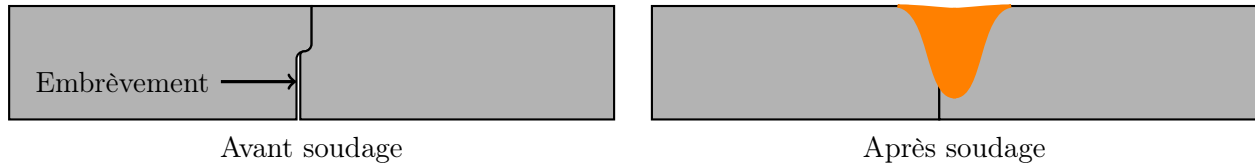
Pièces à assembler avant (à gauche) et après (à droite) soudage. Le schéma de gauche fait apparaître l’embrèvement qui se referme après soudage.
